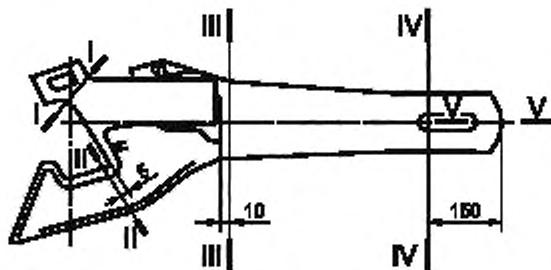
Места разрезки корпуса автосцепки для контроля внутренних дефектов
